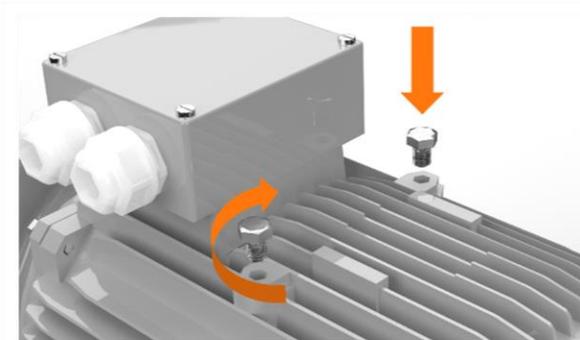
Austausch von Ringschrauben durch Sechskant-Schrauben bei Motoren mit erhöhter IP und Ex - Motoren
